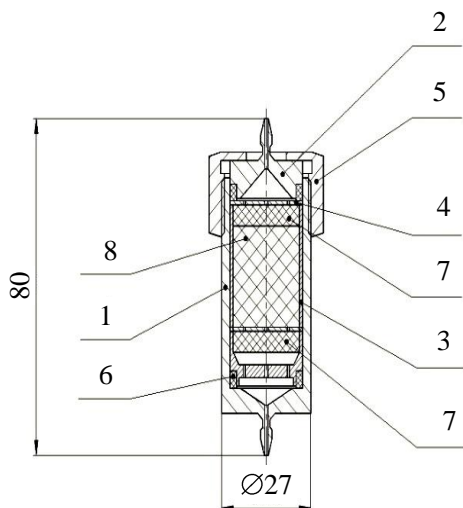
Ториевый реактор: 1 – корпус; 2 – крышка; 3 – стакан; 4 – поддержка; 5 – гайка; 6 – уплотняющий диск; 7 – фильтры Петрянова; 8 – смола.
